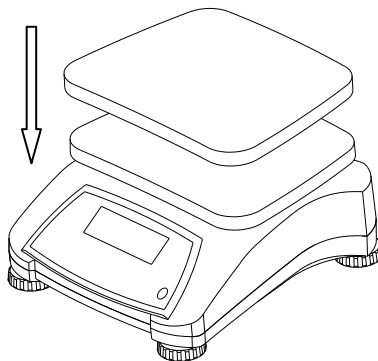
Installez le plateau en acier inoxydable sur la plate-forme de pesée
